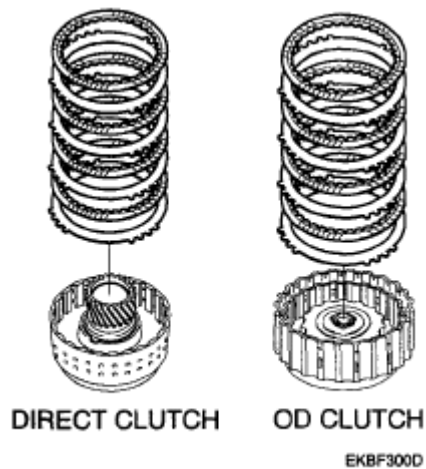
La identificación directa del embrague y el componente del embrague OD
